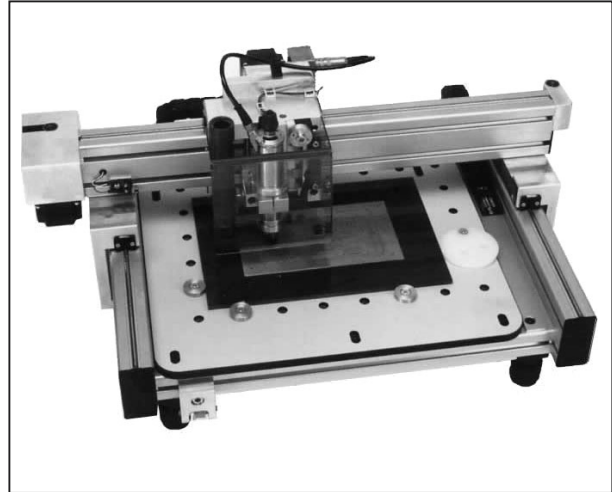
/8.3.19-9: De TechnoRoute machine van TechnoPrint-SMT.
